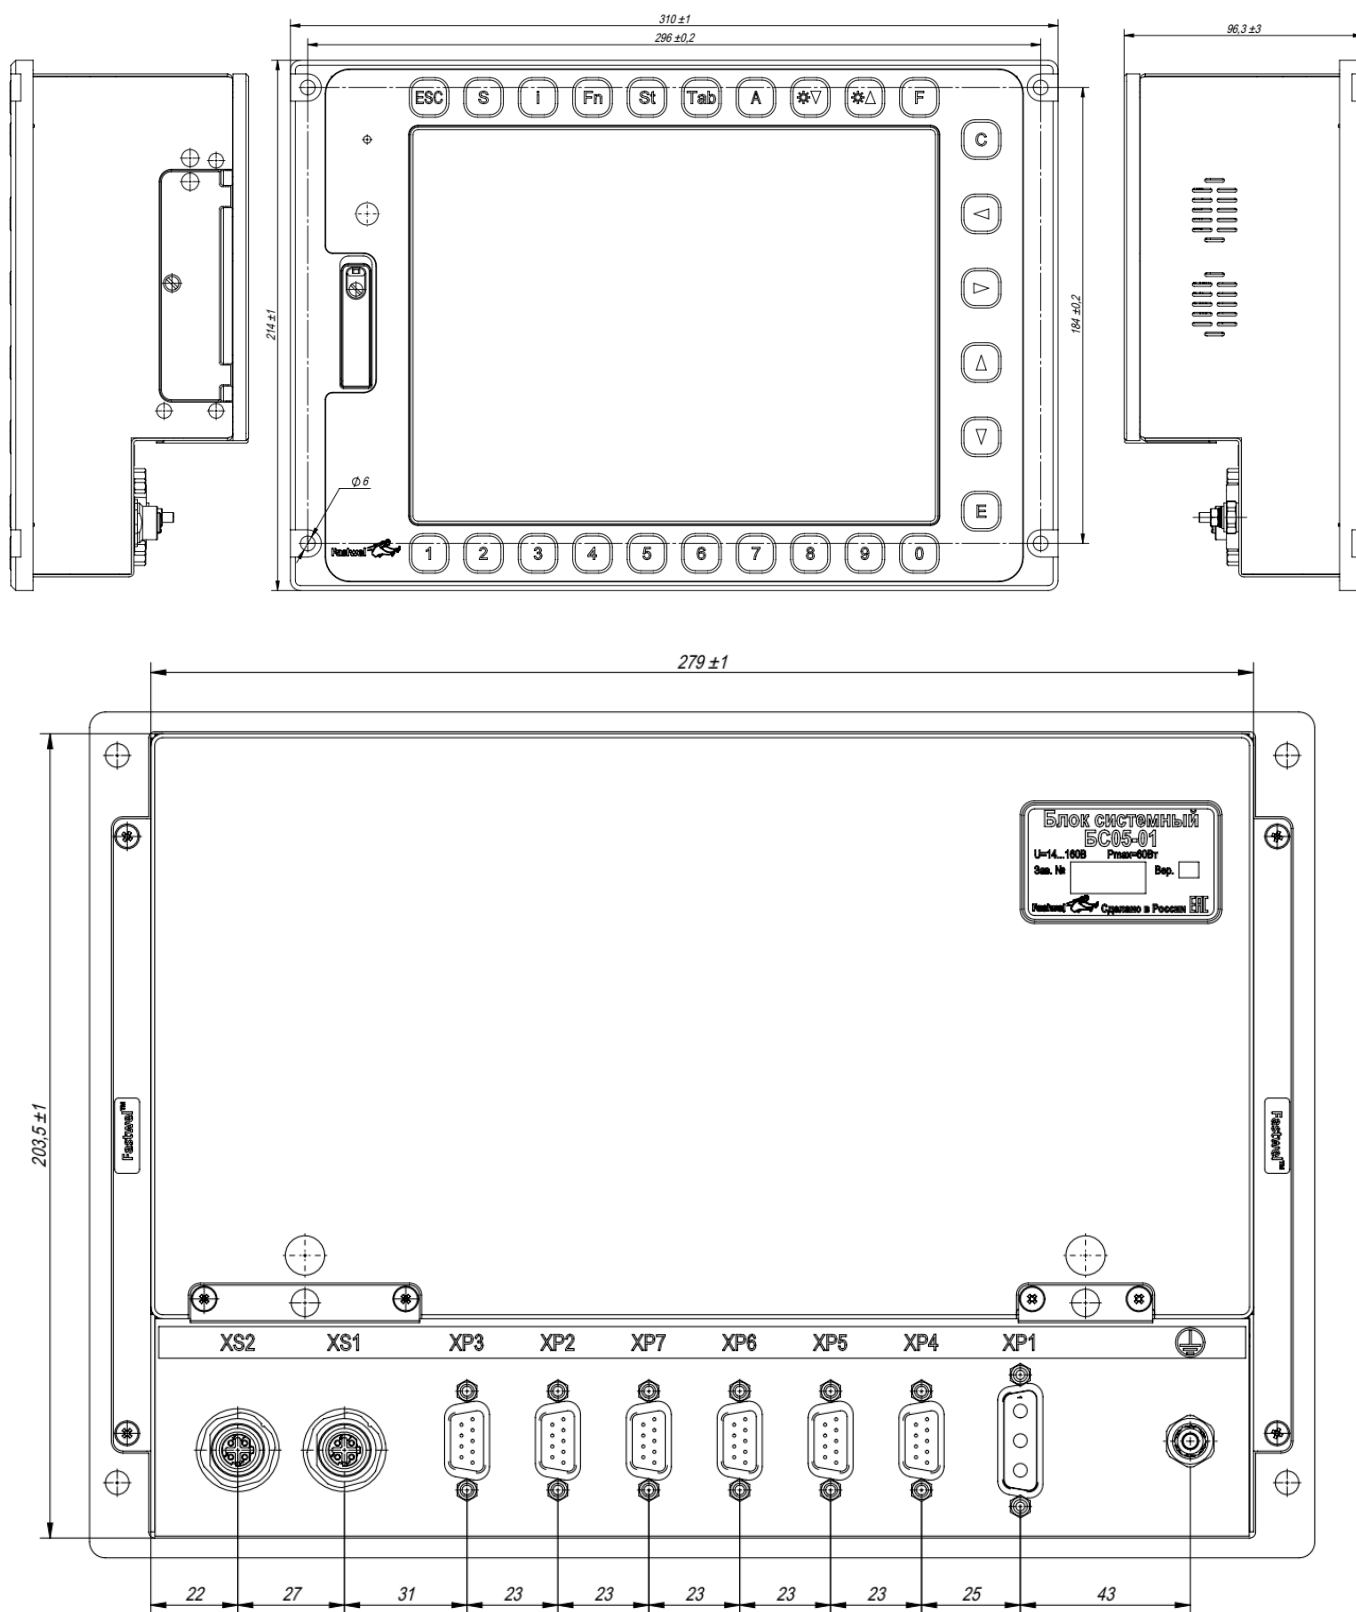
BC05 (габаритные и присоединительные размеры)
